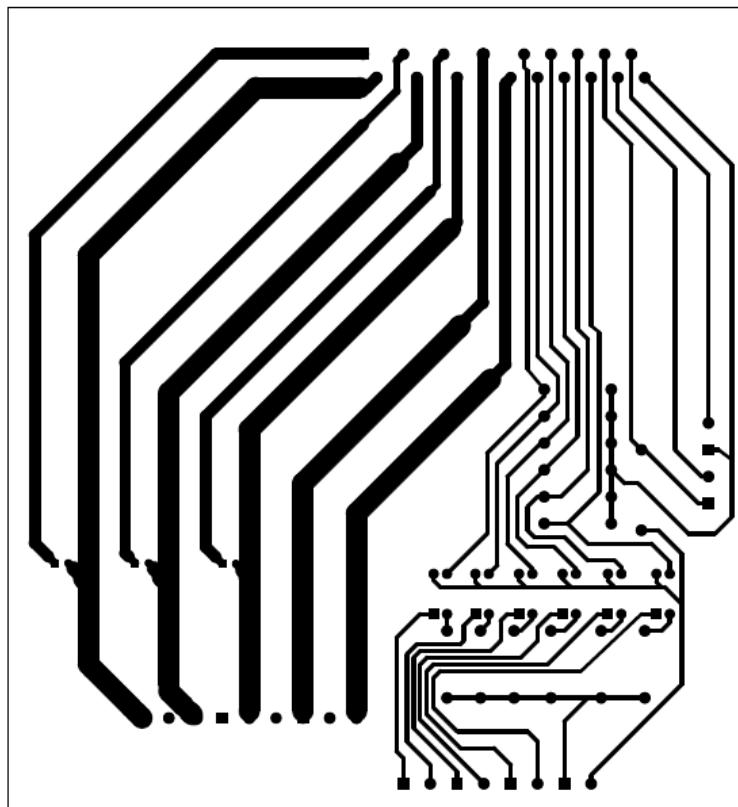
Fitolito Cara de Soldadura. (Elaboración propia)
